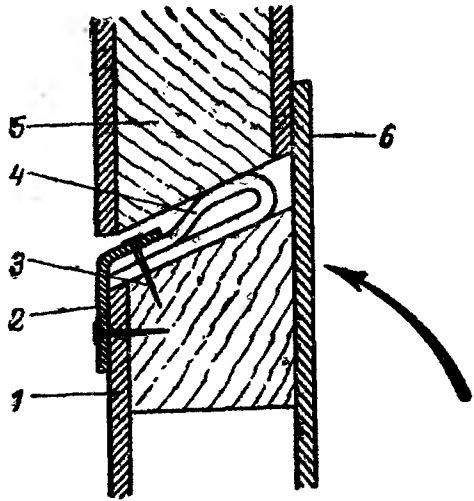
Соединение двери с бортом корпуса: 1 — внутренняя обшивка двери; 2 — окантовка; 3 — шурупы крепления; 4 — резиновое или кожаное уплотнение; 5 — борт корпуса; 6 — наружная обшивка двери.
